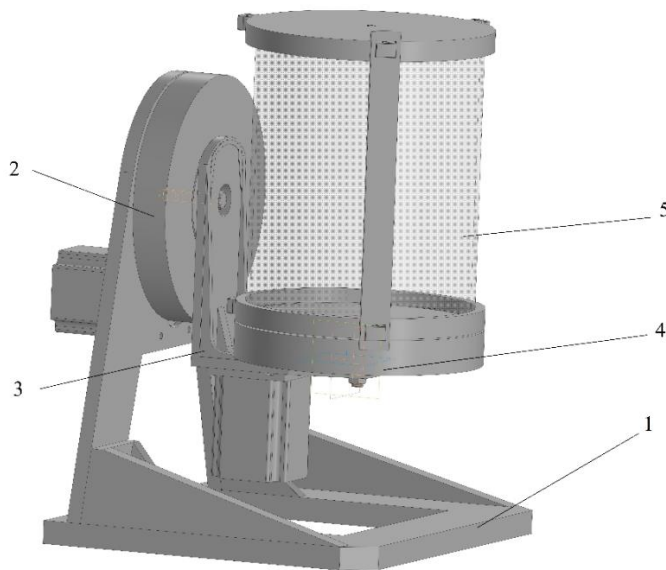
Модель лабораторної установки: 1 – остов; 2 – поворотний механізм; 3 – поворотна платформа; 4 – приводний механізм; 5 – робоча ємність.
